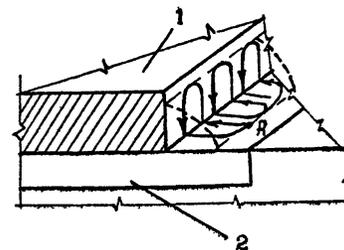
Схема движения конца электрода при сварке валиковыми (угловыми) швами.
